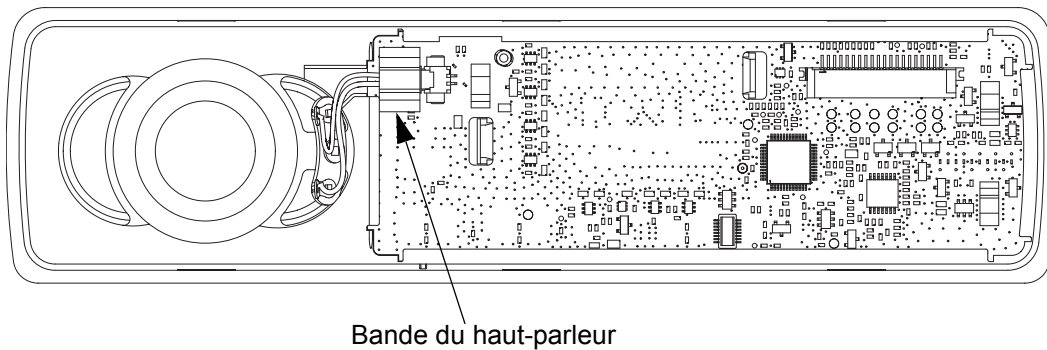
Assemblage de la bande du haut-parleur sur la carte à circuit imprimé
